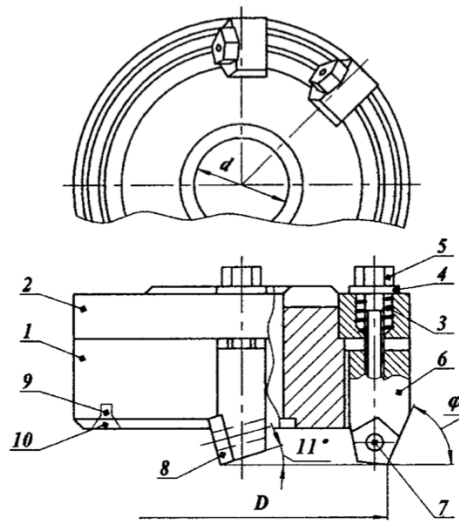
Торцева фреза з механічним кріпленням п'ятигранних БНП
